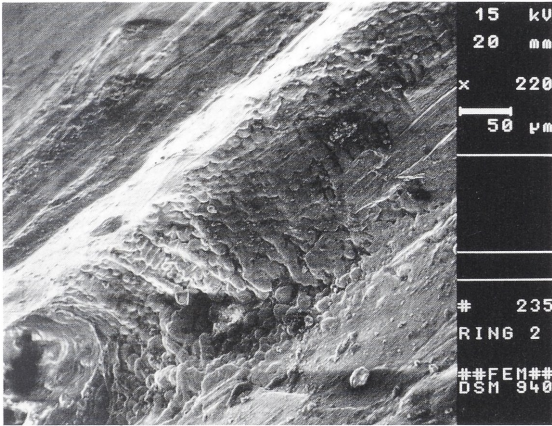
Müssingen. Dendritische Ausbildung der erstarrten Reaktionslot-Schmelze am Grund der Fuge (seitlich mechanisch nachbearbeitete Drahtoberfläche).
